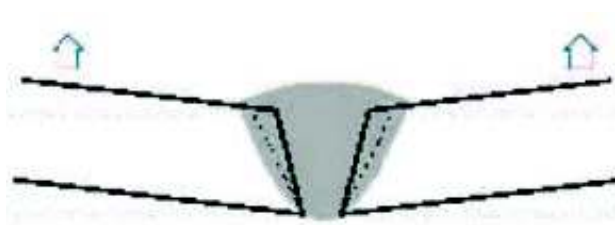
Defecto de distorsión en piezas soldadas⁷⁴
